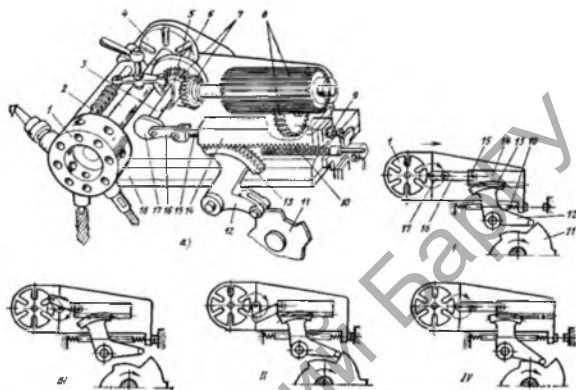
Кинематическая схема токарно-револьверного автомата мод. 1Е140П
